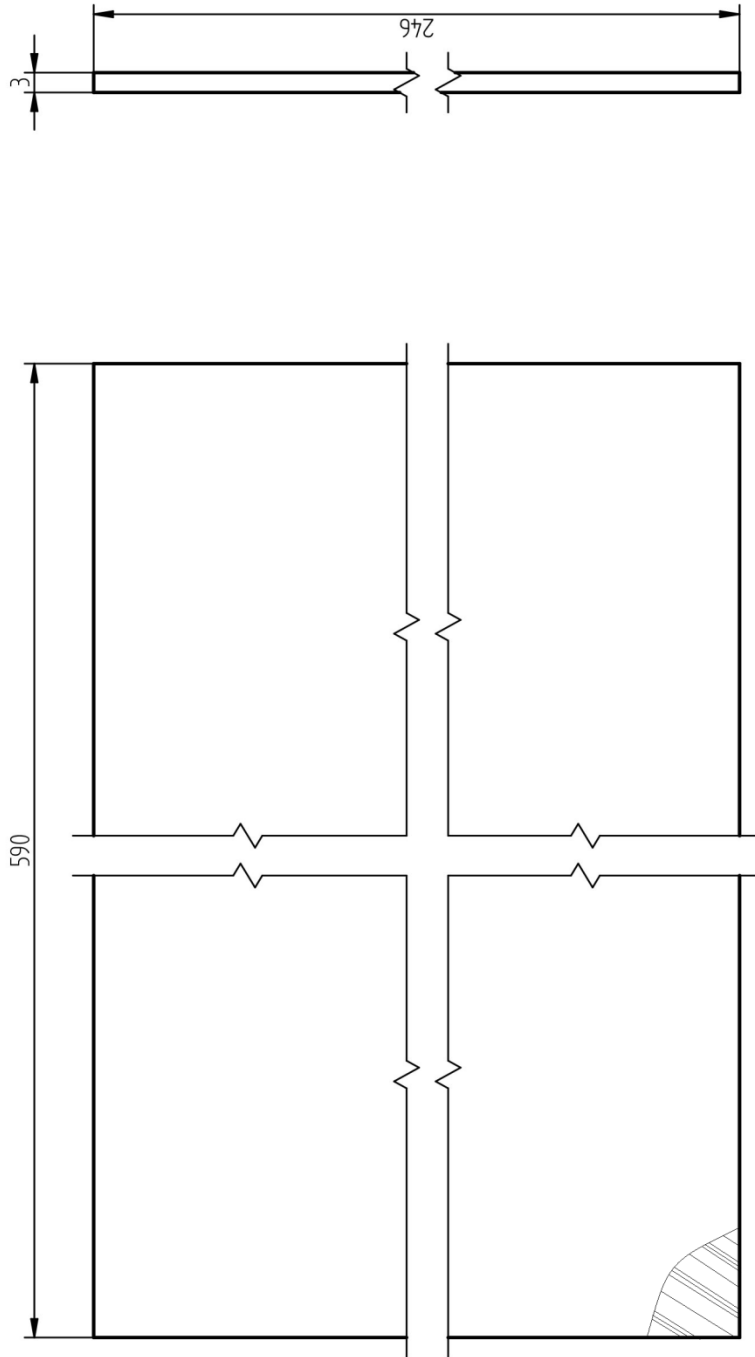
Rysunek wykonawczy boku prawego i lewego
